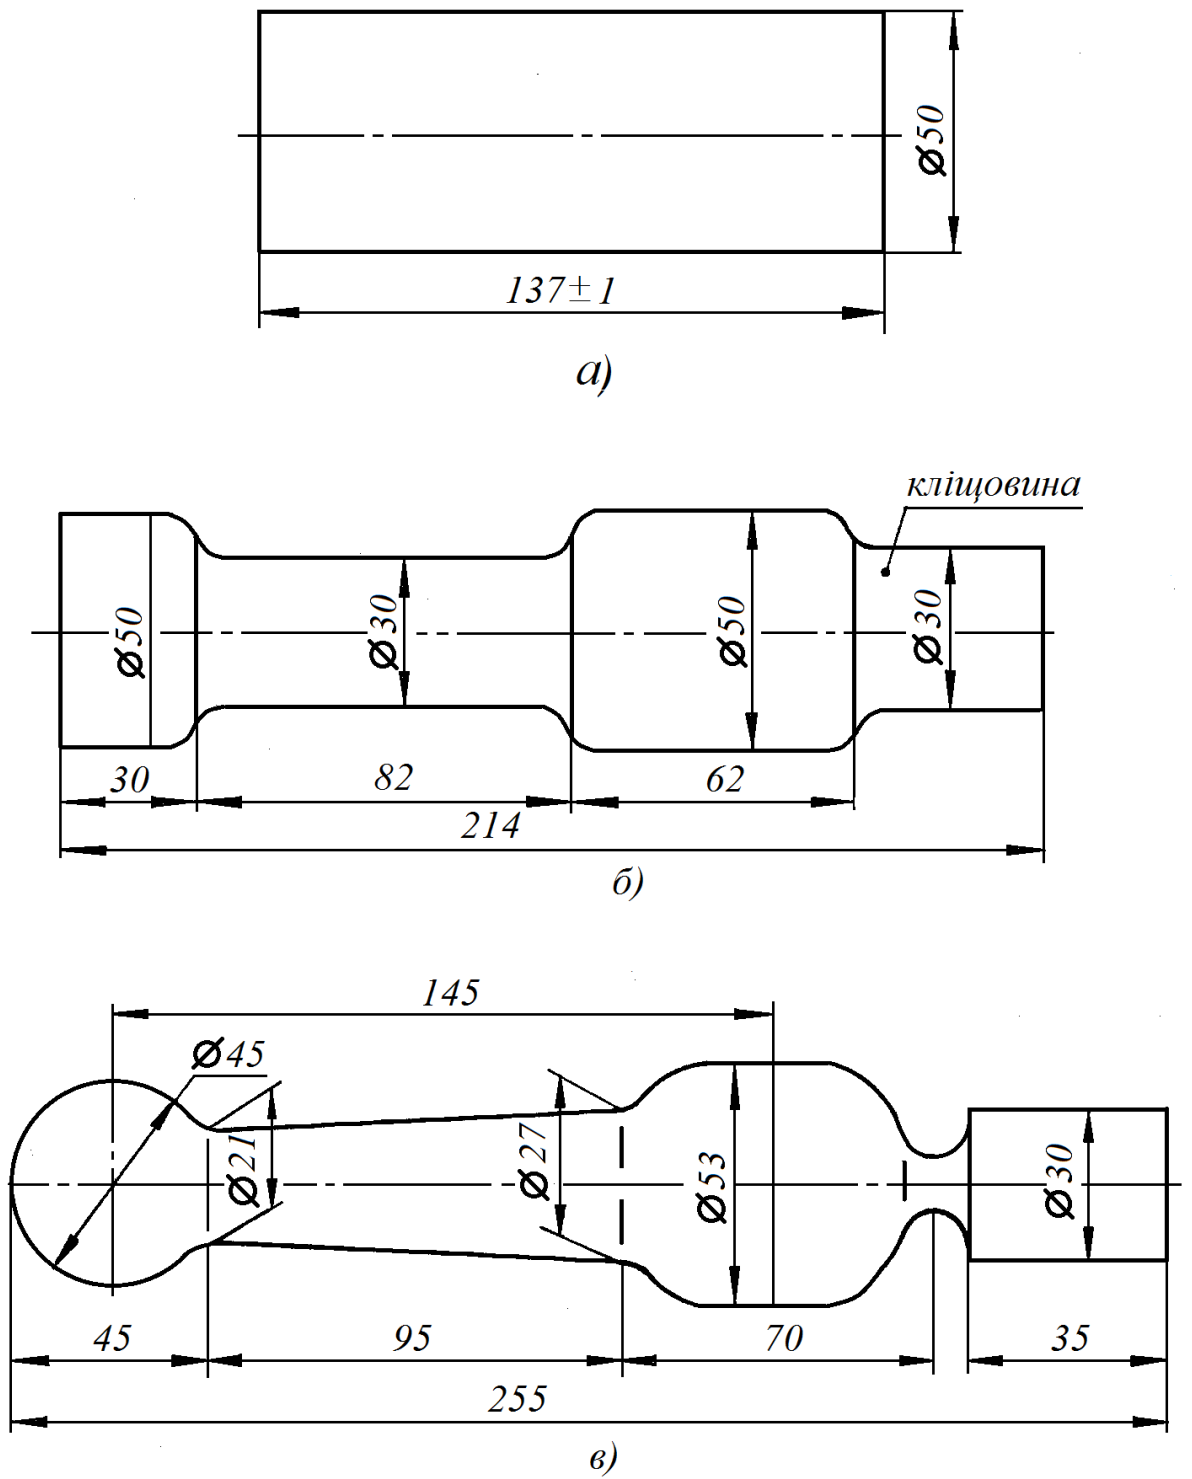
Ескізи вихідної заготовки (а) та заготовок, одержуваних після протяжного (б) та підкатного закритого (в) рiвчакiв.
